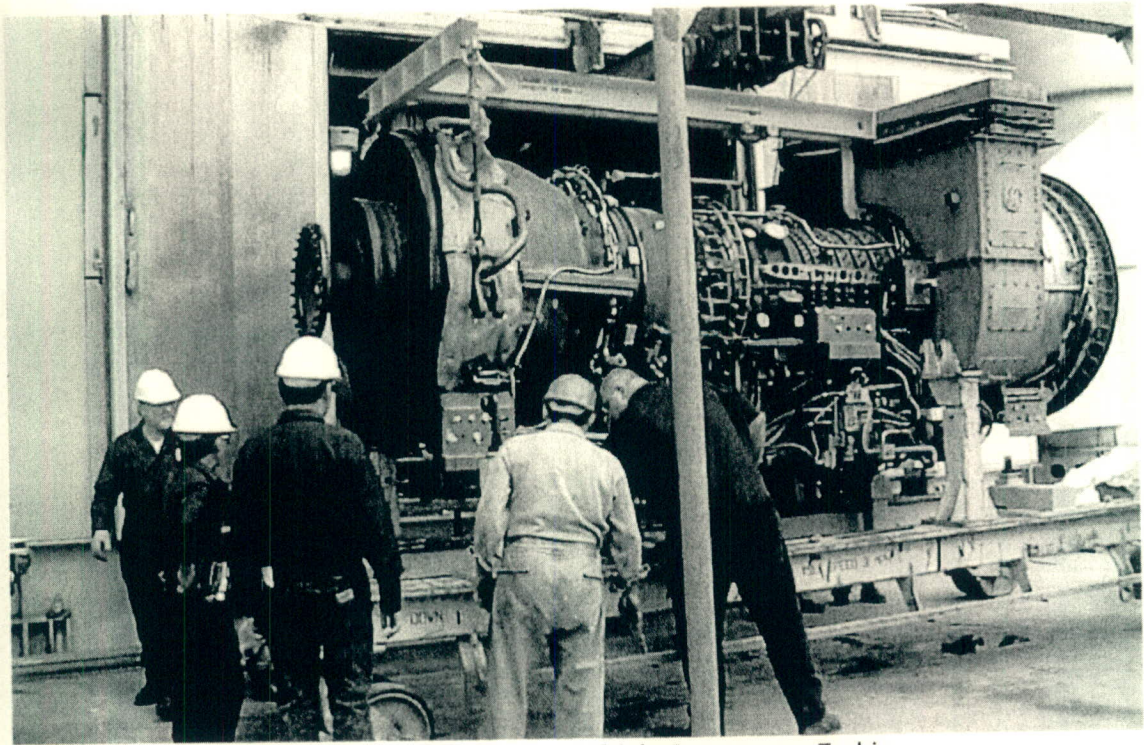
Maniobra de retiro de módulo Compresor – Turbina
